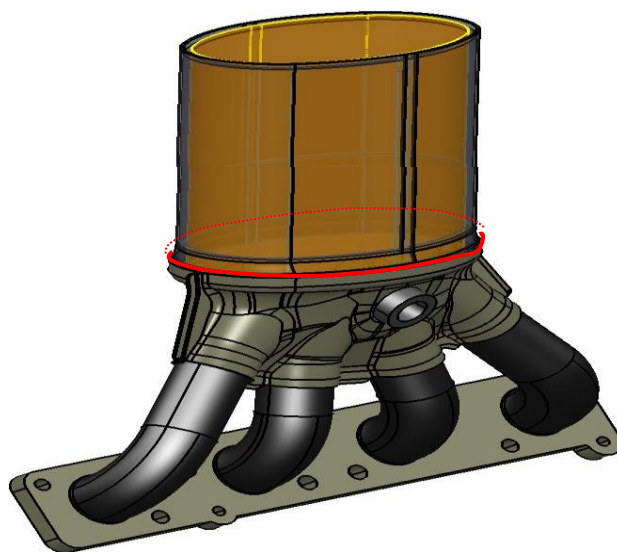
Сварка верхнего узла с корпусом нейтрализатора
